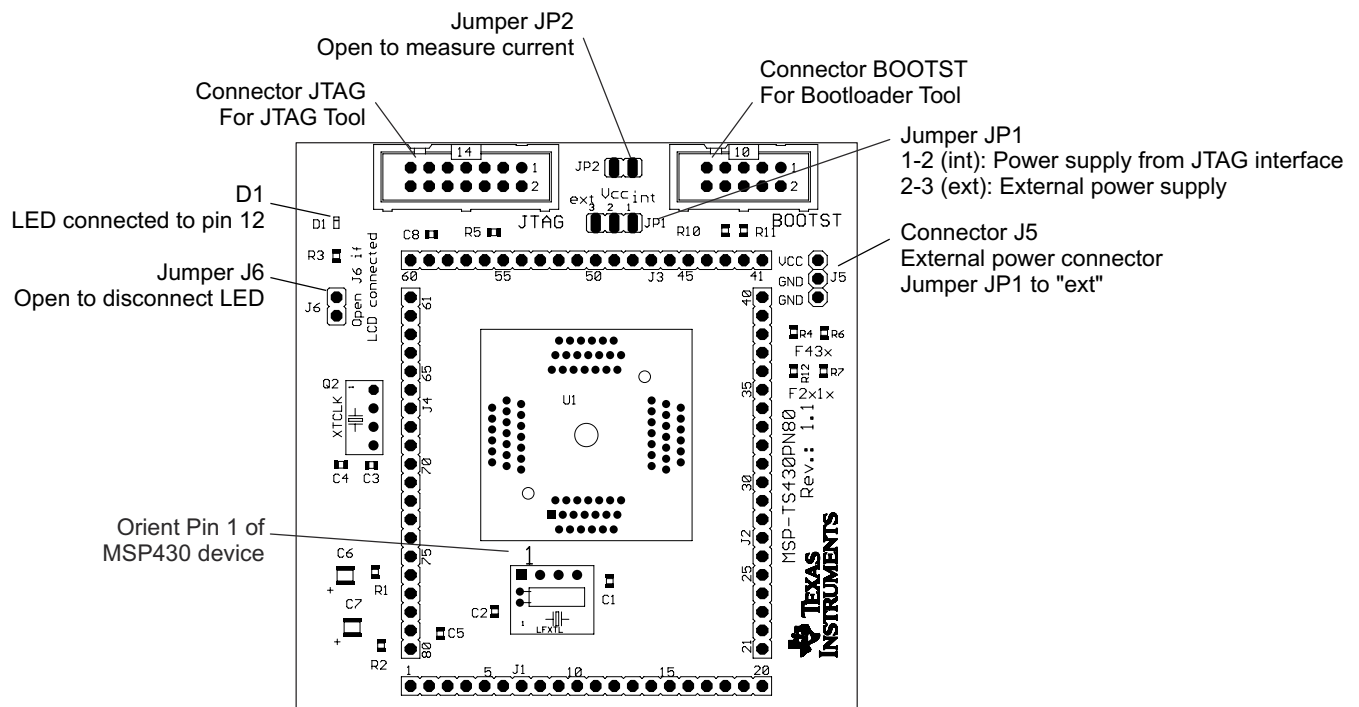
MSP-TS430PN80 目标插座模块, PCB
